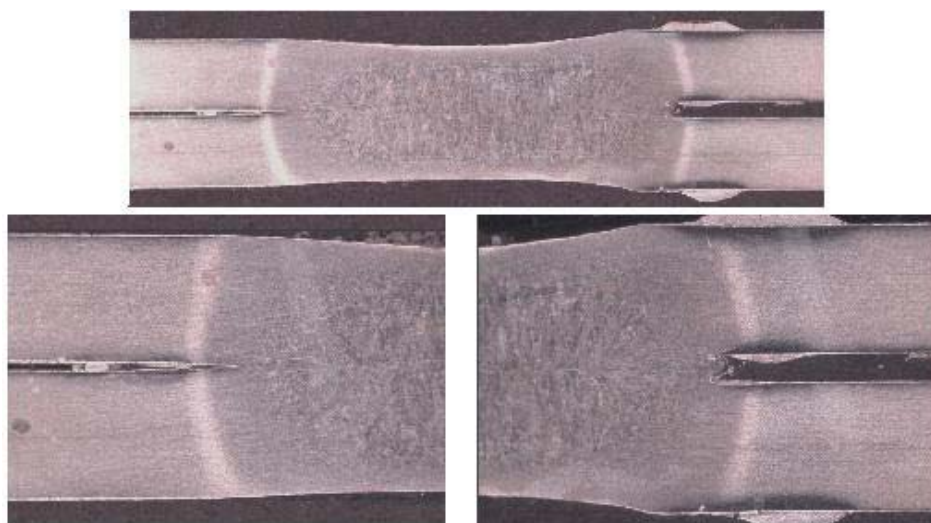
Entalhes gerados na lente de uma solda realizada no aço Dual-Phase 600 revestido soldada através do equipamento AC com eletrodos truncados (espessura da chapa 1,19 mm).
